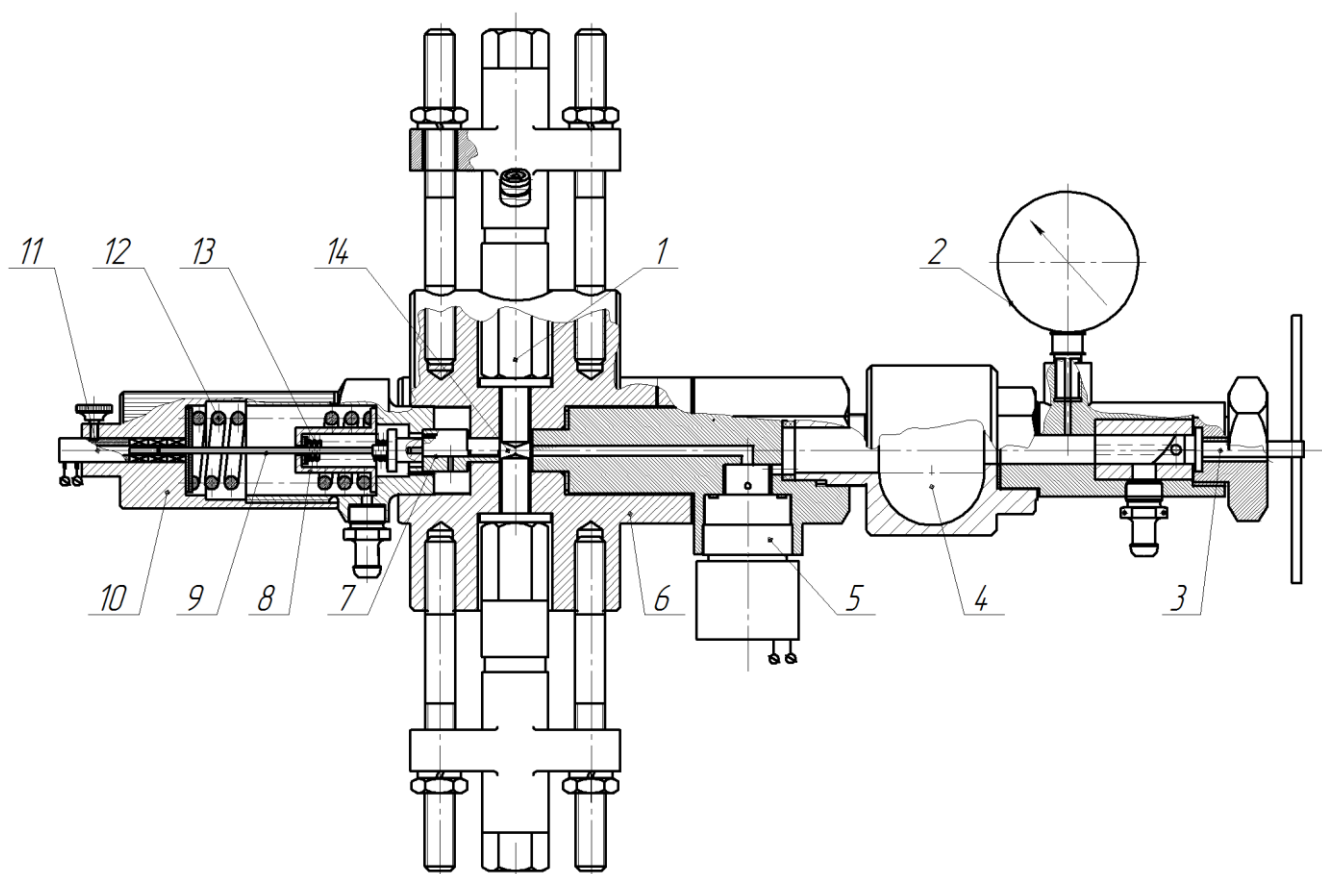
УПВ с двухпружинным аккумулятором: 1- форсунки; 2- манометр; 3- дроссель; 4- гидроаккумулятор (на линии слива); 5- сливной клапан; 6- корпус устройства; 7- плунжер; 8- обойма первой пружины; 9- шток плунжера; 10 – крышка; 11- индуктивный датчик хода плунжера; 12 и 13- пружины; 14- камера впрыска
